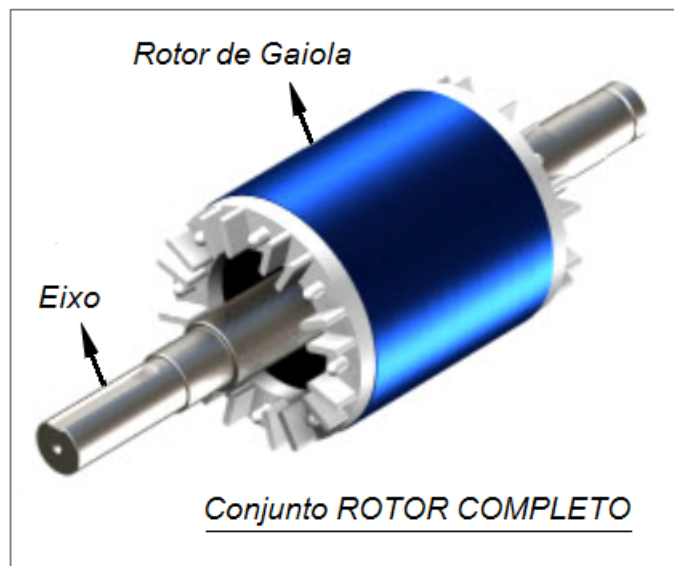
Conjunto Rotor completo de um motor elétrico. Exemplo de conjunto Fantasma.
